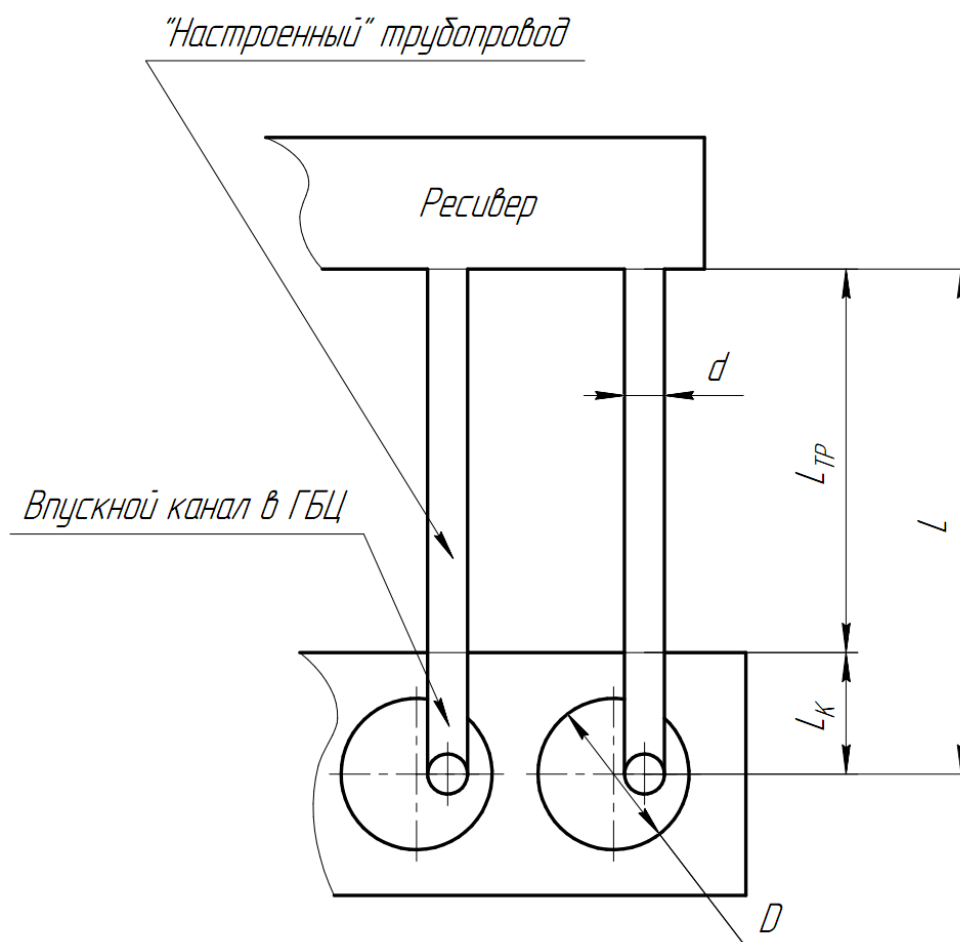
Расчетная схема для индивидуальных настроенных трубопроводов
